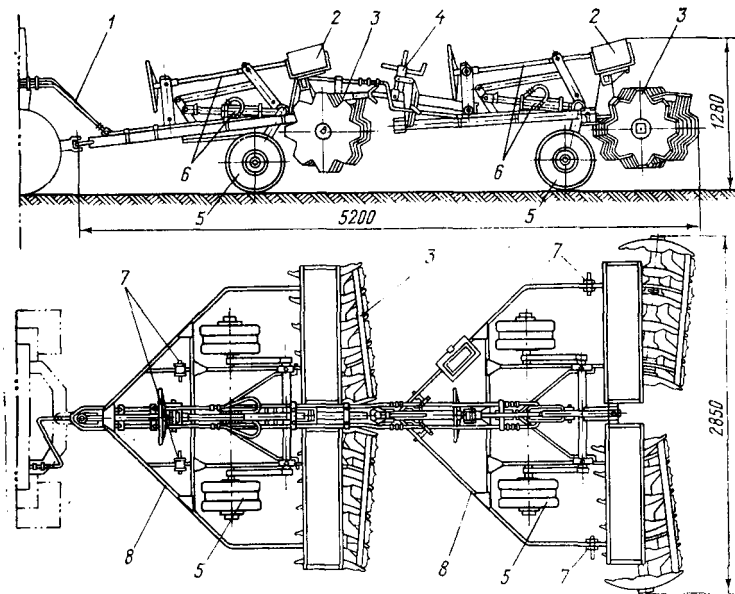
Борона дисковая тяжелая БДТ-25А с гидроуправлением: 1 — шланги гидроподъемника; 2 — ящик для балласта; 3 — передняя и задняя дисковые батареи; 4 — механизм понизителя прицепа; 5 — ходовые колеса; 6 — механизм подъема рамы и регулировки глубины; 7 — шарнир; 8 — рама.
